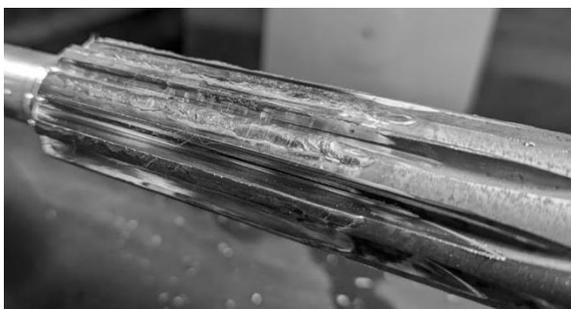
Первичный вал после наплавки зубьев шлица
